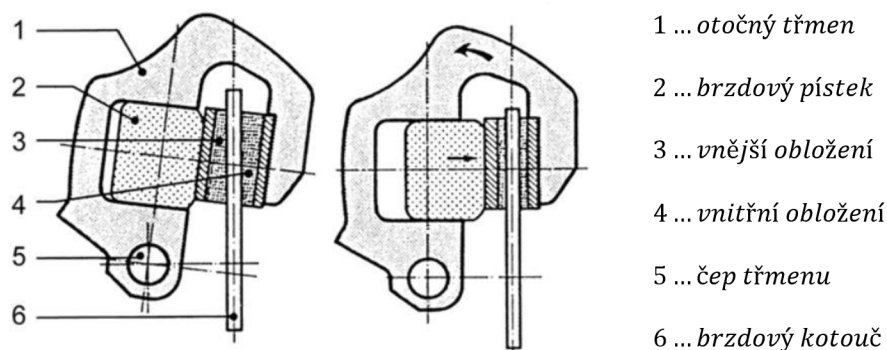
Kotoučová brzda s výkyvným třmenem [3]
